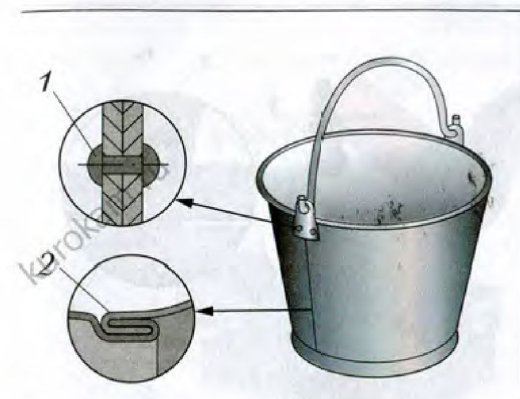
Примеры соединения деталей из тонколистового металла: 1 – заклёпочное соединение; 2 – фальцевый шов
